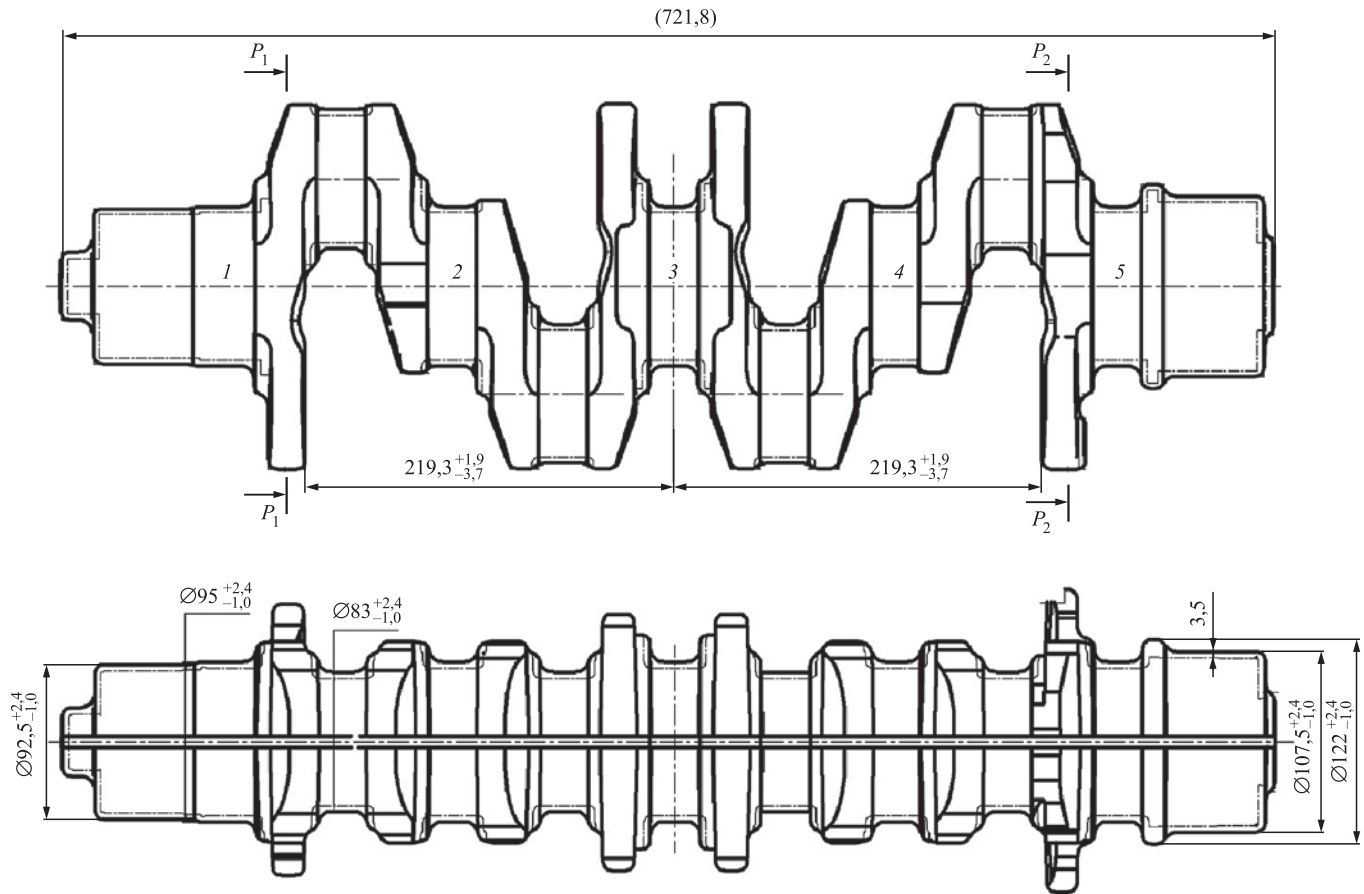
Эскиз поковки коленчатого вала Р4 с ее ключевыми параметрами:
